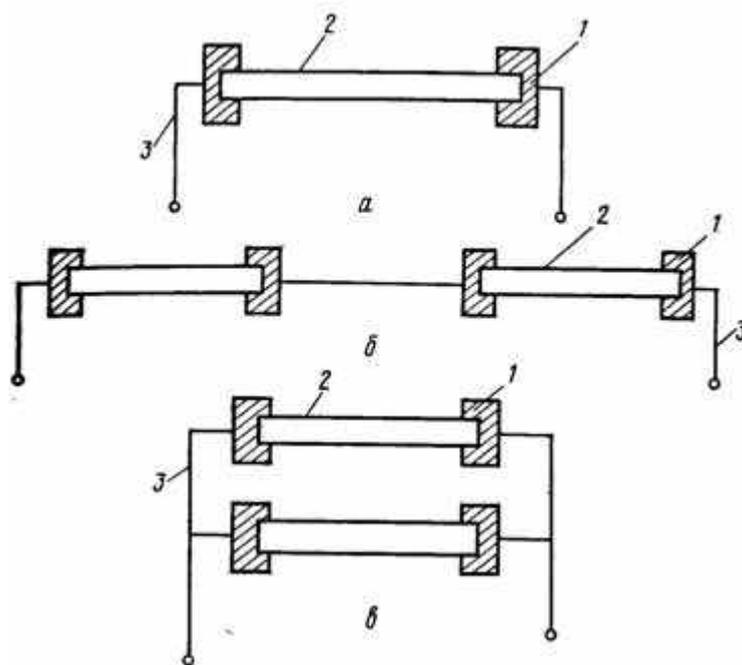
Схемы однопозиционного (а) и многопозиционных устройств с последовательным (б) и параллельным (в) включением заготовок в электрическую цепь: 1 — зажимной токоподводящий контакт; 2 — нагреваемая заготовка; 3 — токоподводящий провод.
